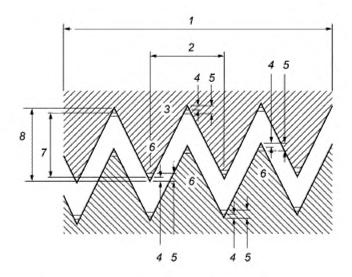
Размеры резьб для ЖСЭСР труб
